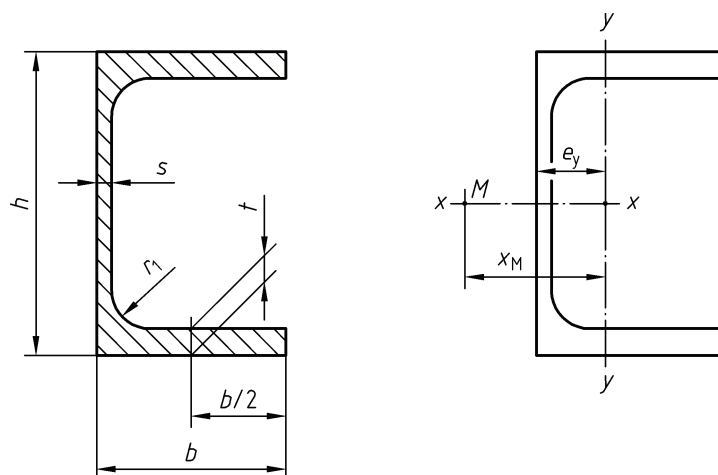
Warmgewalzter U-Profilstahl mit parallelen Flanschflächen
